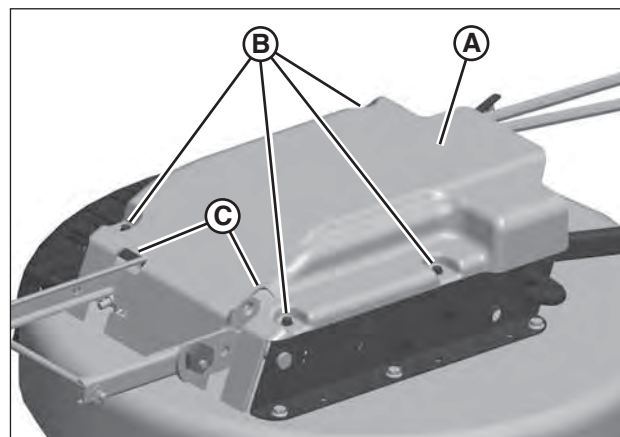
Dépose du couvercle de plateau de coupe (plateau de coupe retiré de la machine uniquement pour la clarté de l'illustration)
